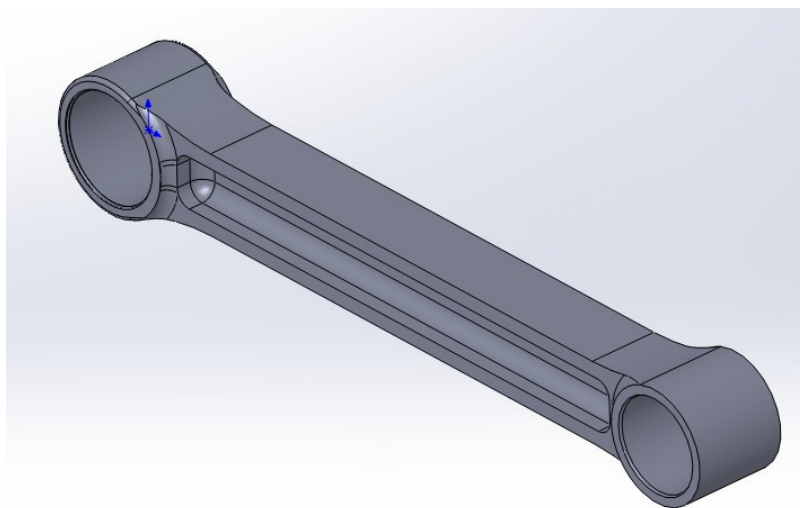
Твердотельная модель прицепного шатуна звездообразного двигателя
